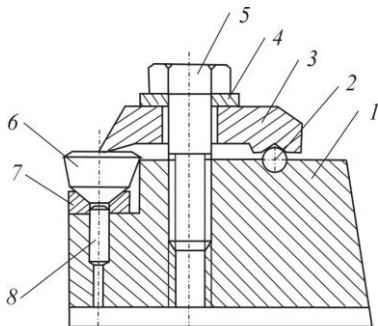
Узел крепления режущей пластины из ПКНБ с вертикальной и горизонтальной осями симметрии: 1 – корпус державки; 2 – шарик; 3 – прихват; 4 – шайба; 5 – прижимной болт; 6 – режущая пластина; 7 – сепаратор; 8 – штифт
